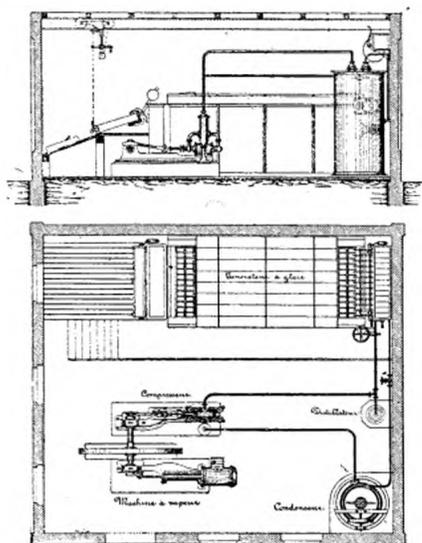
et 104. — Ensemble d'une installation *Linde* pour fabrication de la glace.
